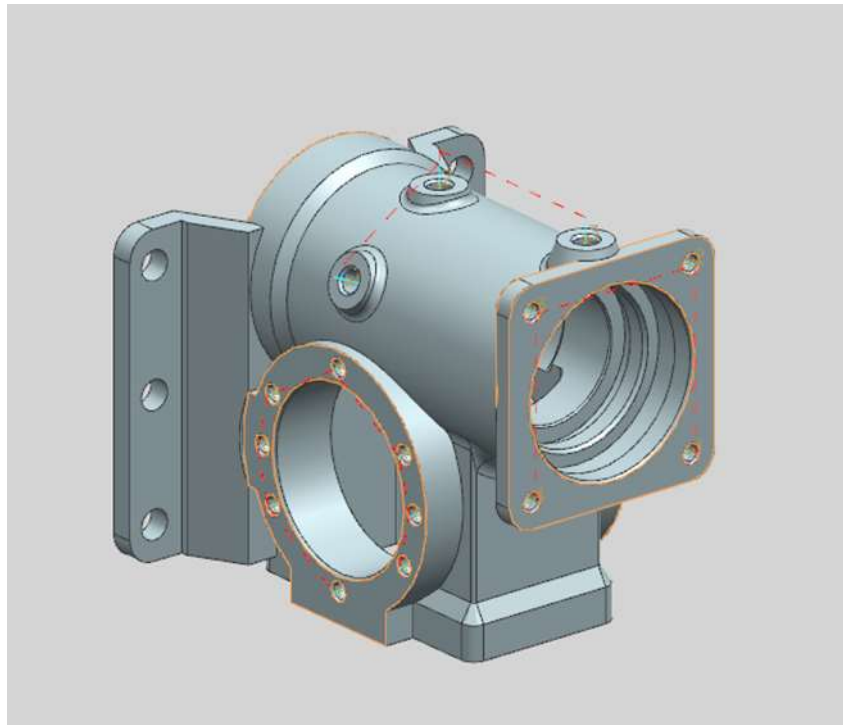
Траектории движения инструмента на детали «Корпус»
